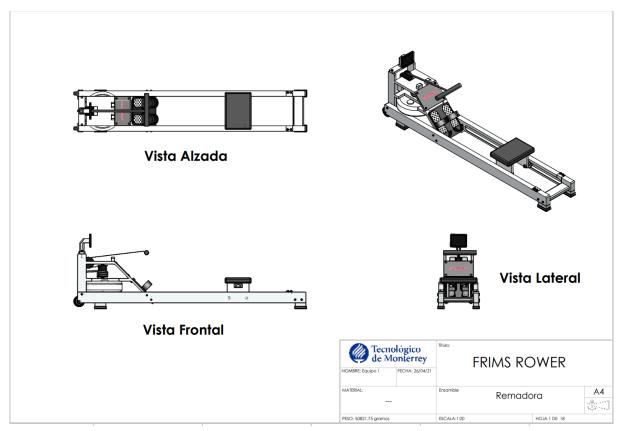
Vistas de la remadora completa con vista alzada, frontal, lateral e isométrica.
